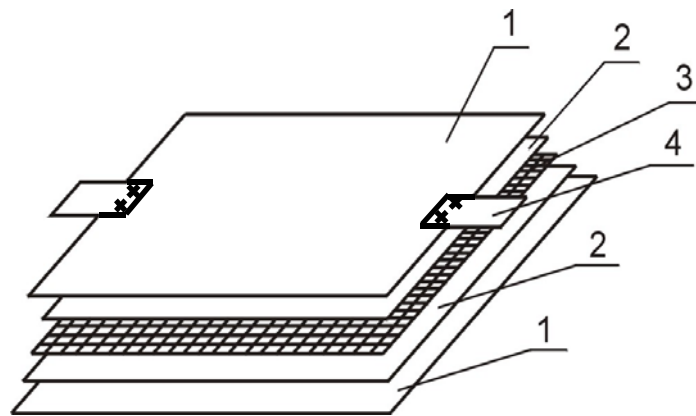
Схема збірки пакета для зварювання заготовки композиційного матеріалу з шаруватою ніобій-титановою матрицею:
